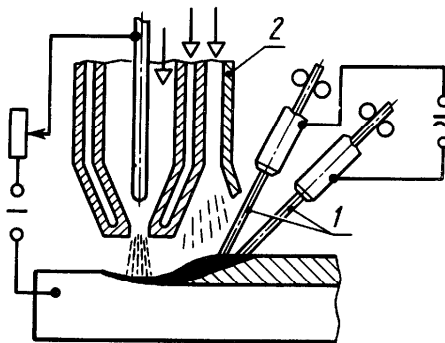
Плазменная наплавка с двумя присадочными проволоками
